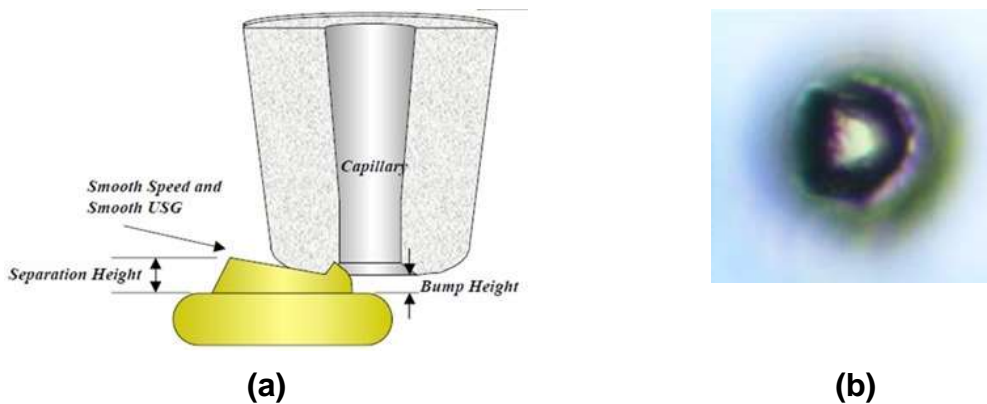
Corte de Bump en modo Single Smooth. (a) Movimientos del capilar. (b) Vista superior del corte. [21, 2]
